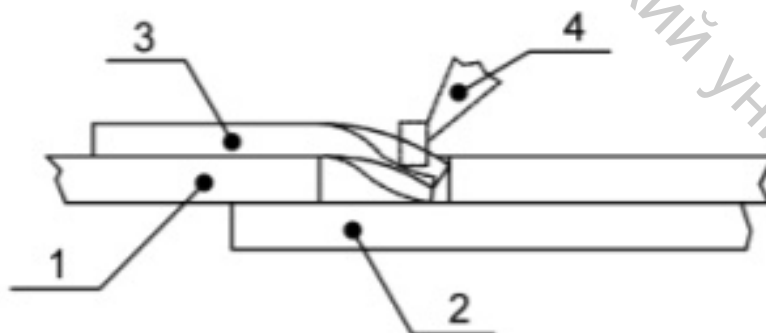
Схема воздействия верхнего упора на детали при сборке
